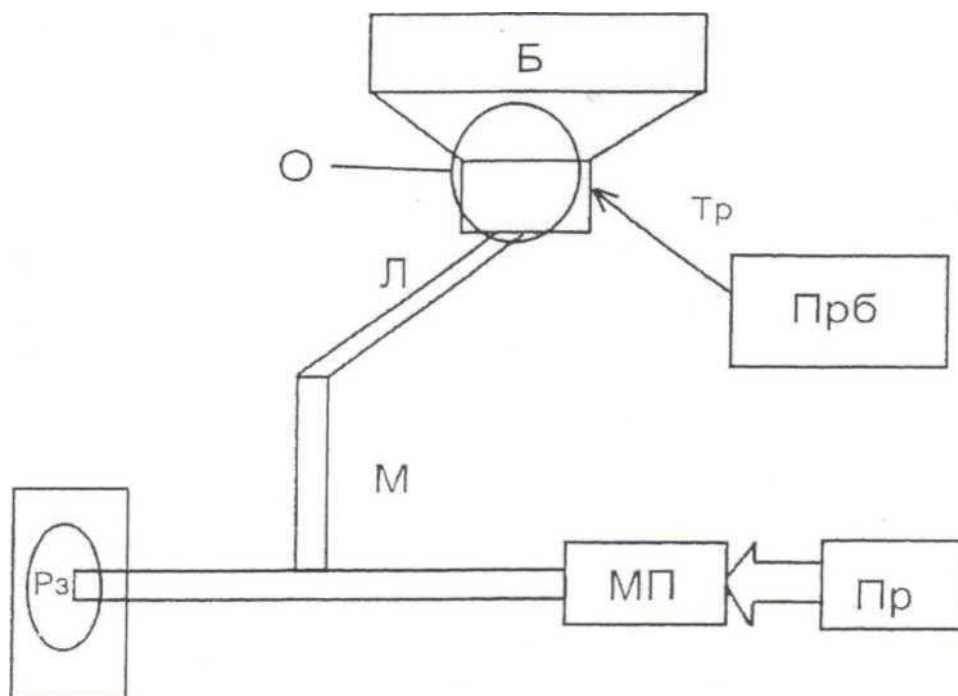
Схема БМЗП (бункерно-магазинний завантажувальний пристрій)
